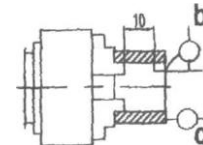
Токарный патрон с креплением заготовки за внутреннюю поверхность с прямыми кулачками
